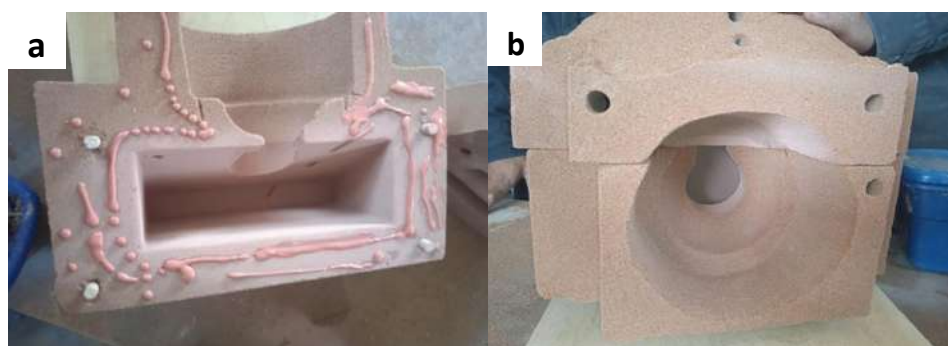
Protector, a) molde con pegamento de corazones y b) ensamblaje de las dos partes del molde.
